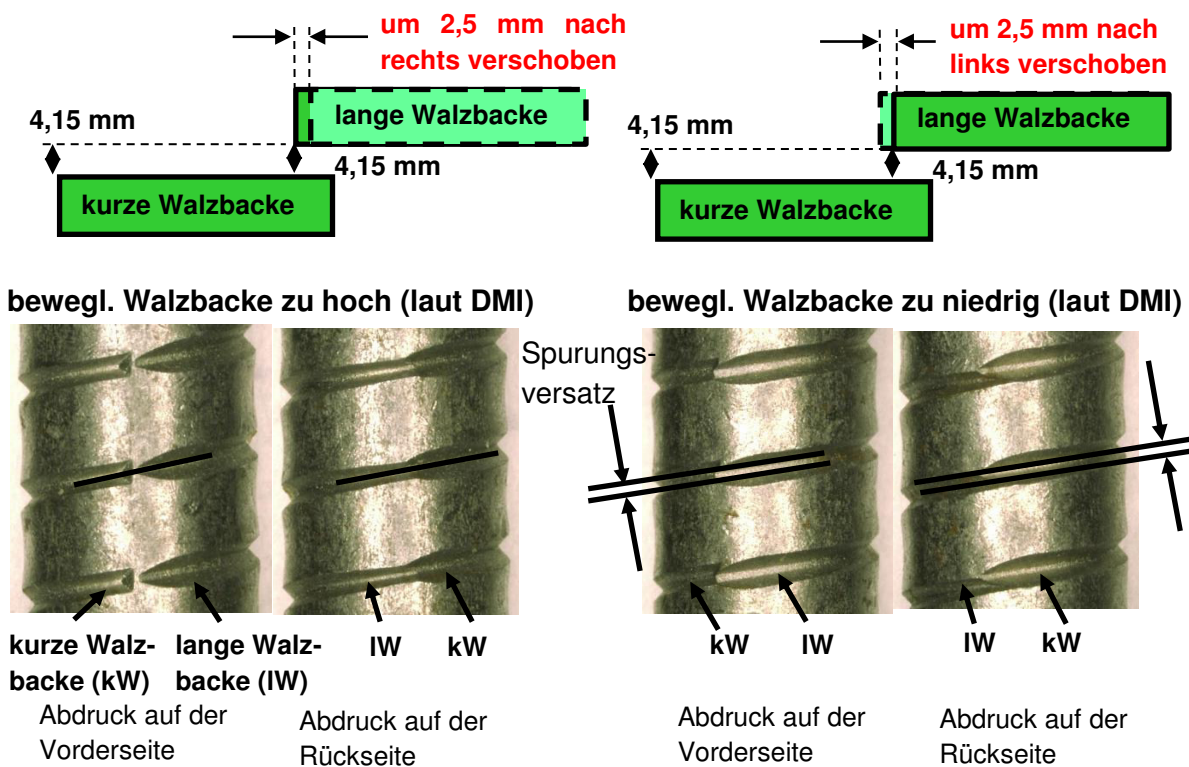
Falsche horizontale Walzbackenausrichtung
